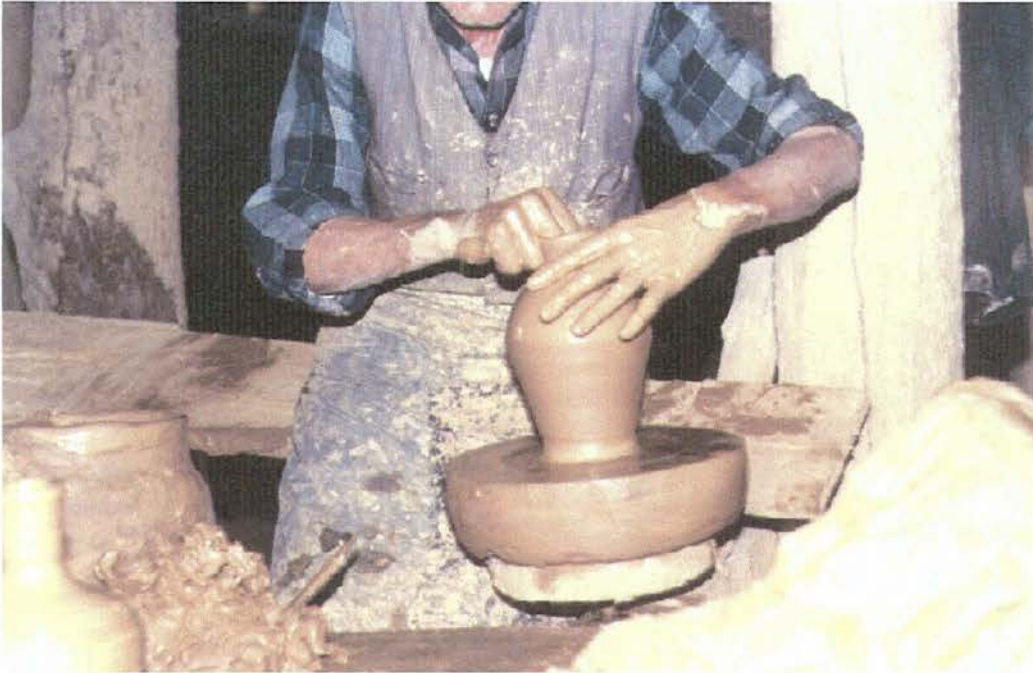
Tornada ömlek Gövdesinin Şekillendirilmesi
